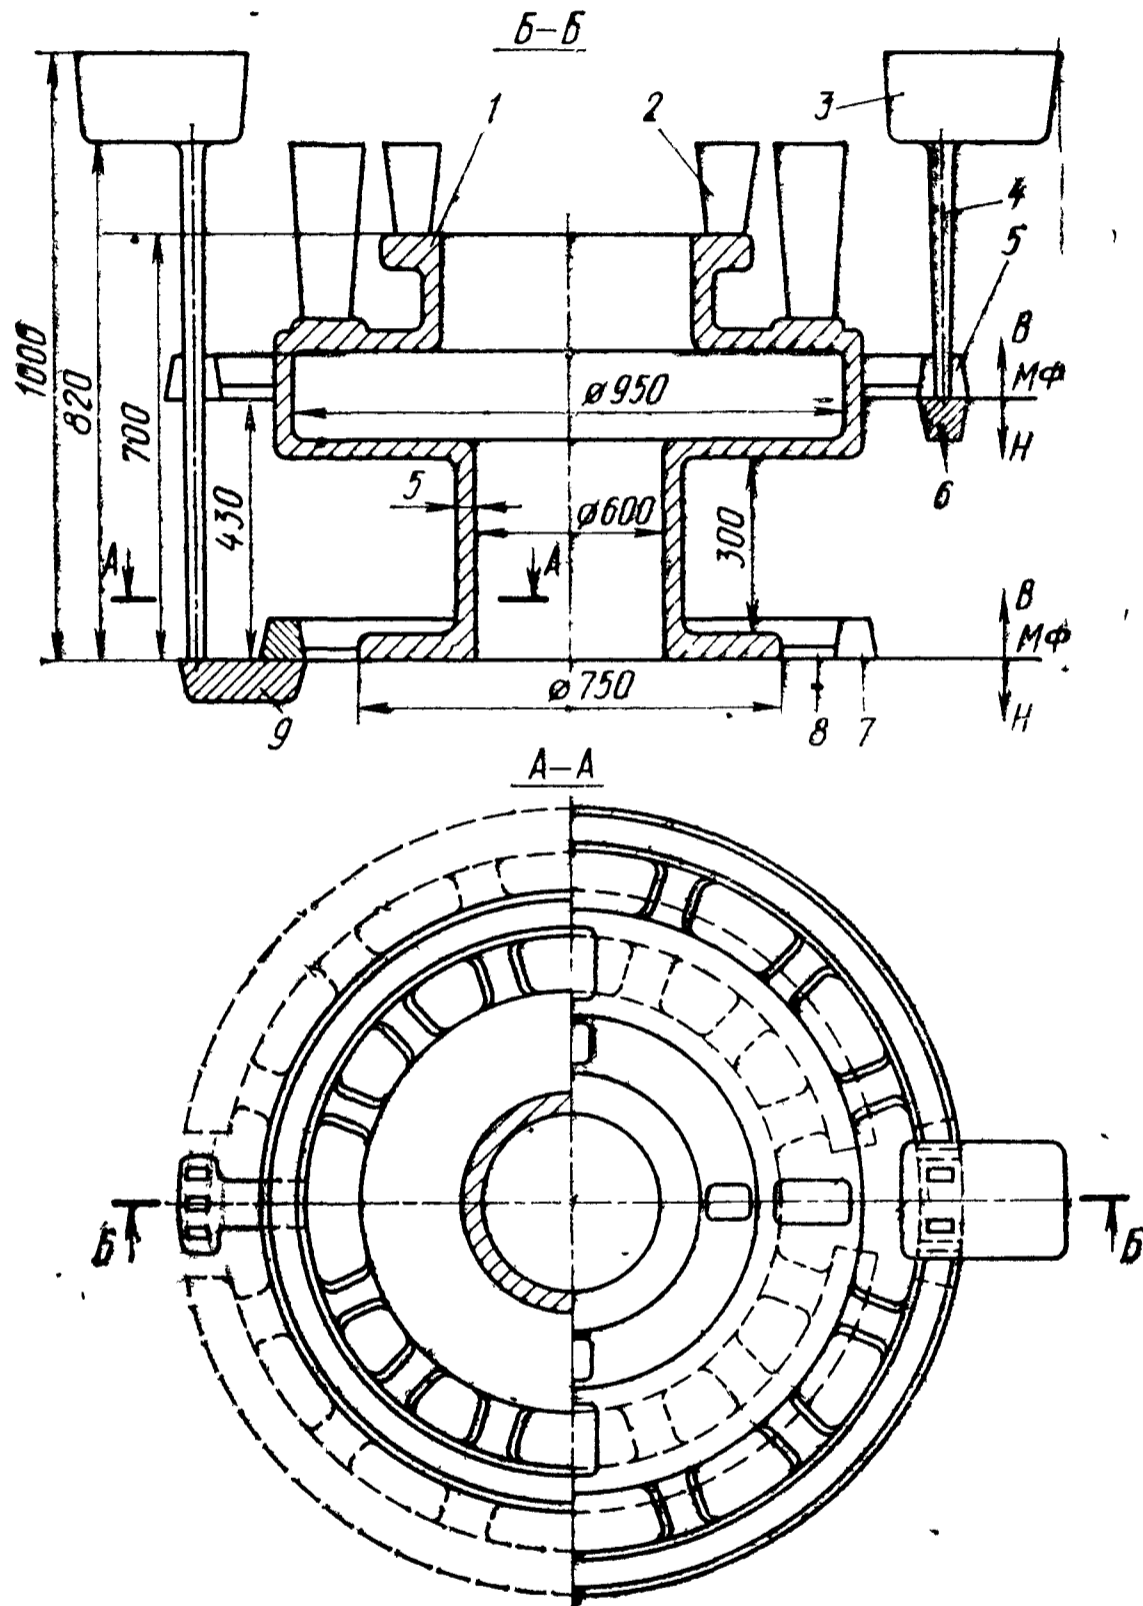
Схема устройства ярусной литниковой системы для отливки корпуса:
